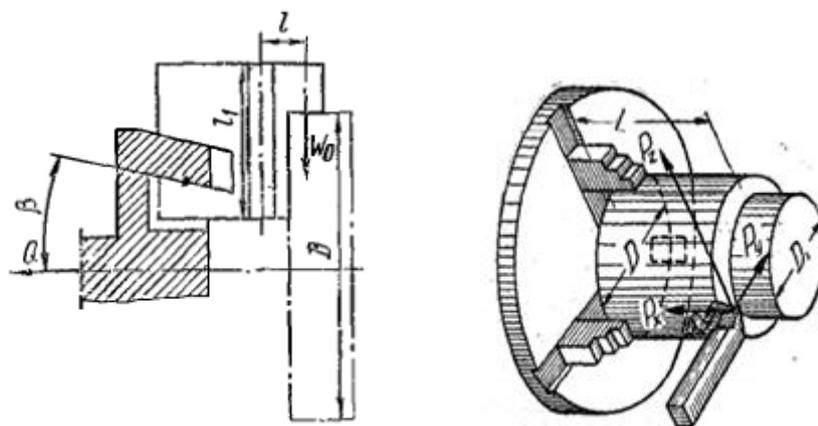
Схема расположения действующих сил при закреплении детали
